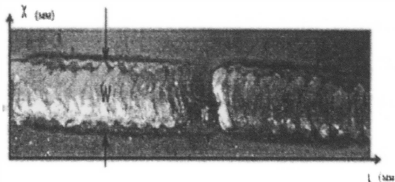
Определение границ шва и вычисление ширины сварного соединения.
